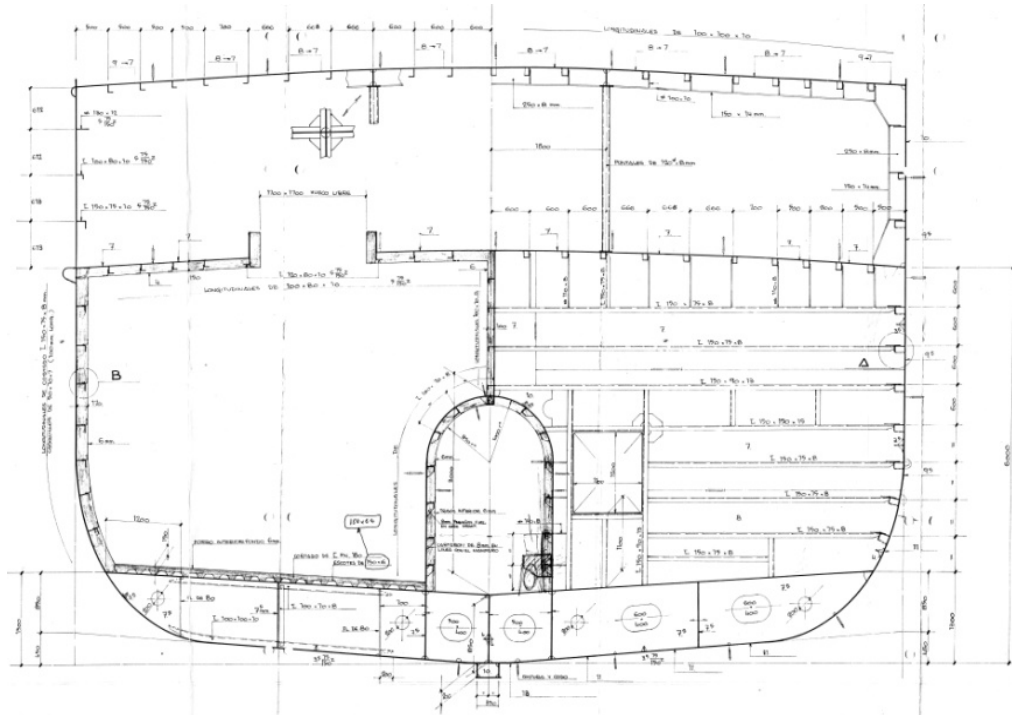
Plano estructural transversal de la cuaderna maestra del buque [3].
